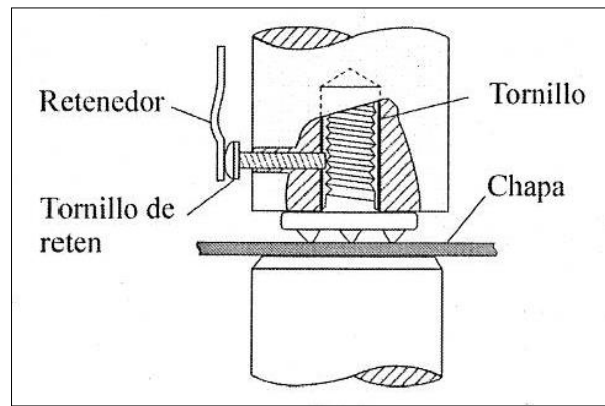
Tornillo a ser soldado por proyección, alojado en el electrodo inferior.
